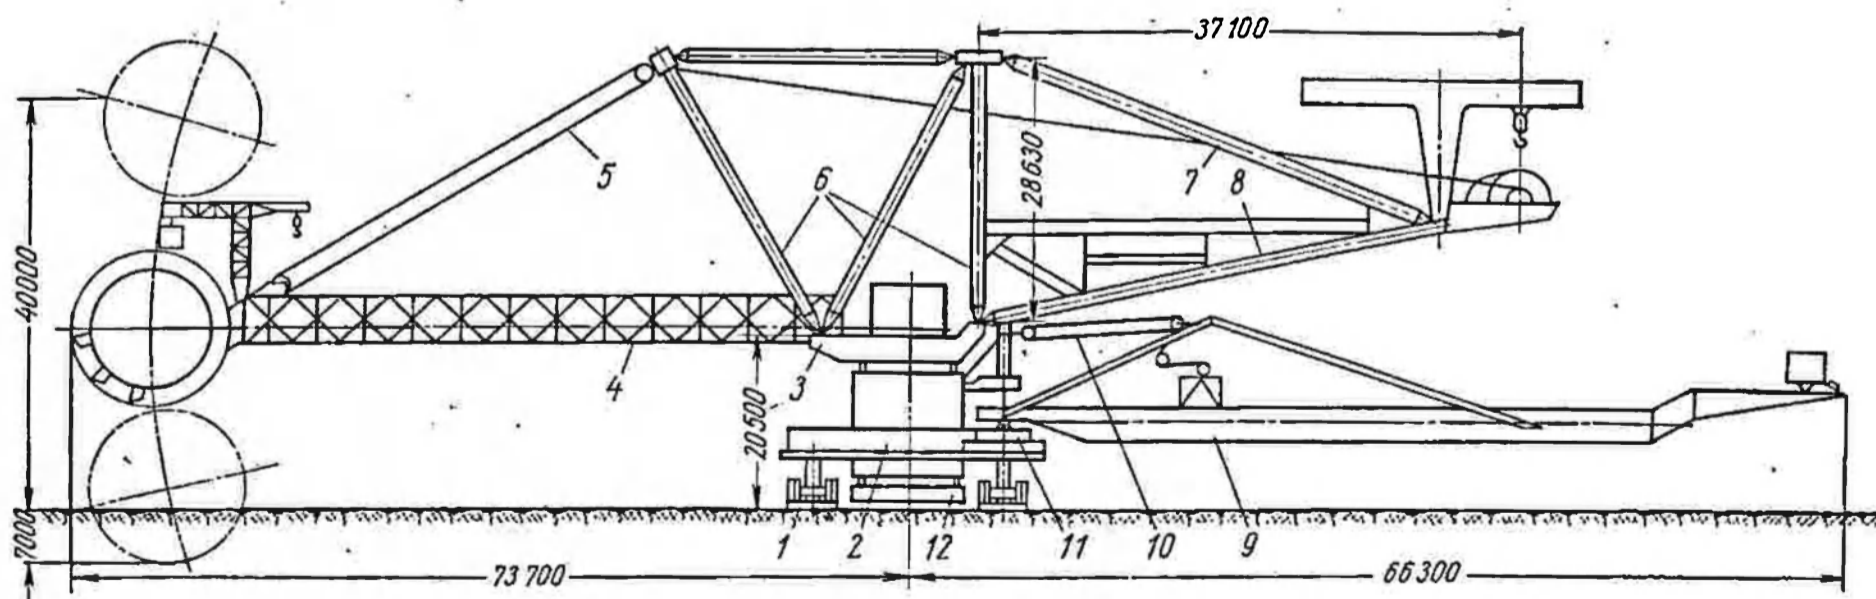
Конструктивная схема роторного экскаватора ЭРШР-1600 $\frac{40}{7}$:
